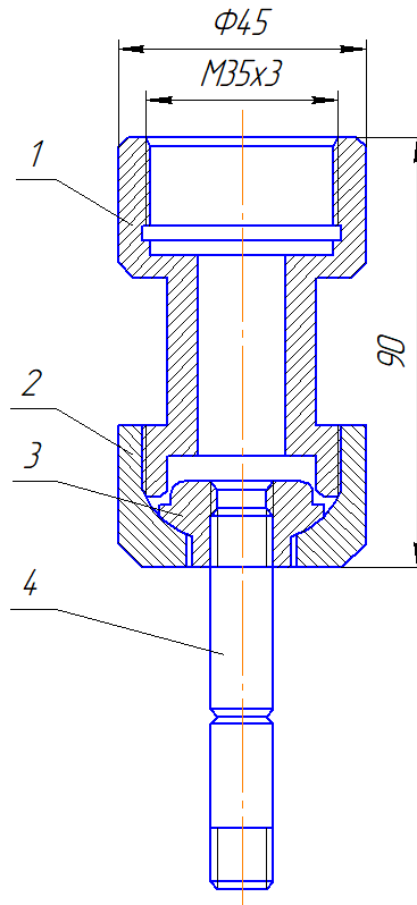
Загальний вигляд захоплювача (розміри в мм) для закріплення циліндричного зразка з кільцевою тріщиною за умов статичного розтягу для розривної машини: 1 – корпус; 2 – гайка сферична; 3 – сухар сферичний; 4 – циліндричний зразок.
